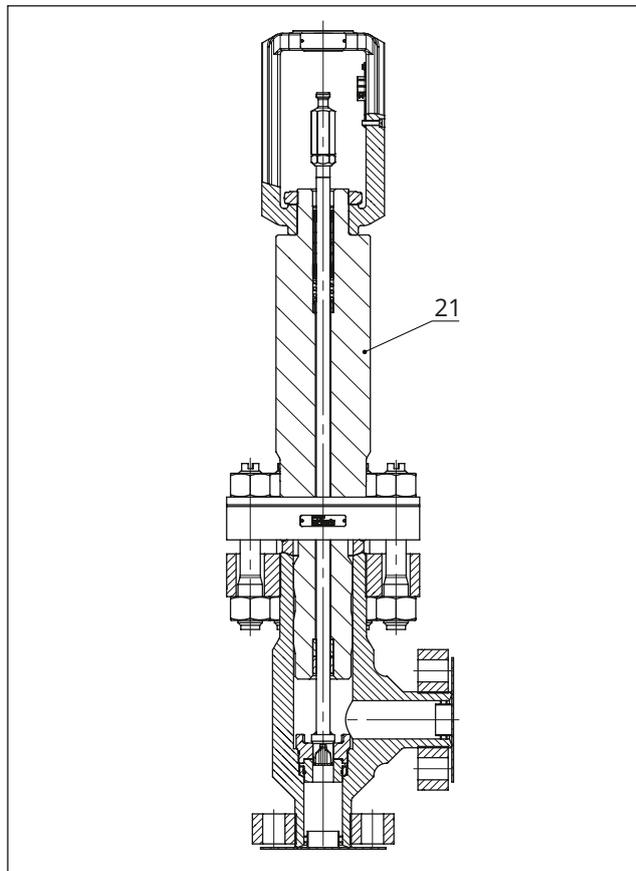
Typ 3259 in Ausführung mit Isolierteil
